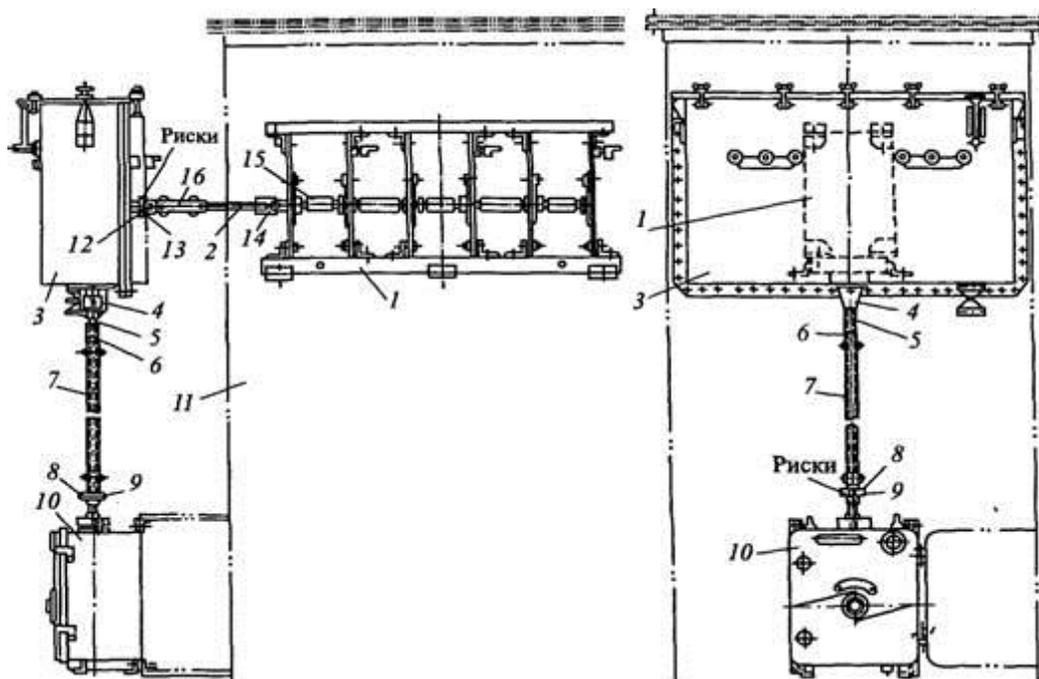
Аппараты переключающего устройства типа РНТ, установленные на трансформаторе: 1 — переключатель; 2 — горизонтальный пал; 3 — бак контакторов; 4 — сальник; 5 — вал сальника; 6 — переходная муфта вертикального вала; 7 — вертикальный вал; 8 — нониусный диск вала (7); 9 — нониусный диск вала механизма (10); 10 — приводной механизм; 11 — бак трансформатора; 12, 13 — нониусные диски вала контакторов и карданного вала; 14 — соединительная муфта вала переключателя; 15 — вал переключателя; 16 — горизонтальный карданный вал.
